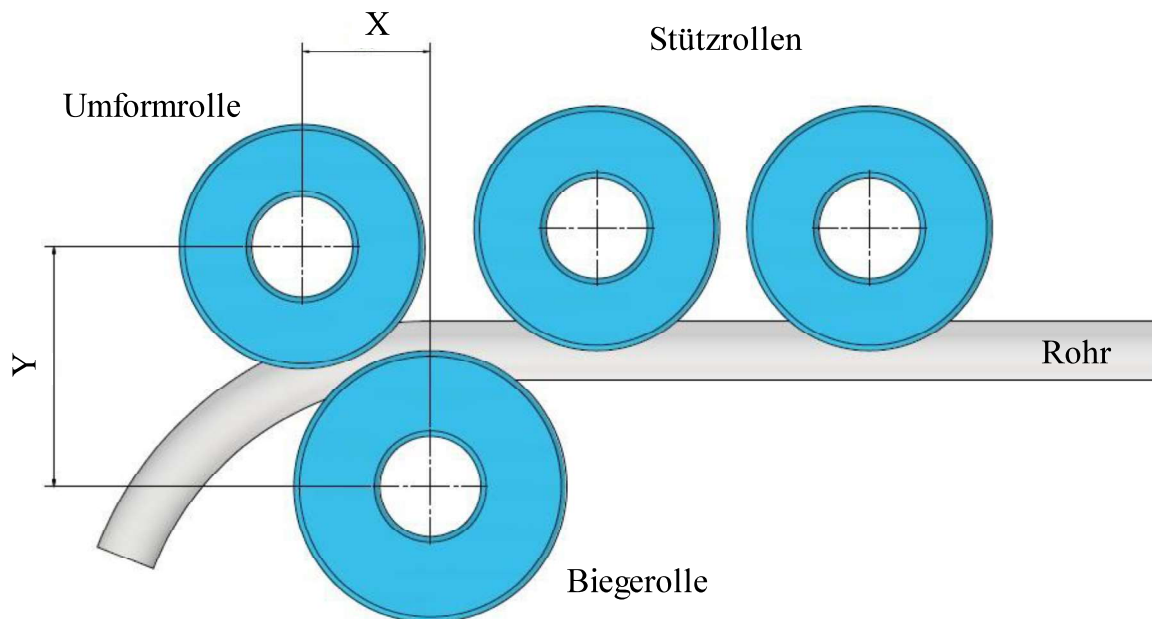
Schematischer Werkzeugaufbau für das Drei-Rollen-Schubbiegen
